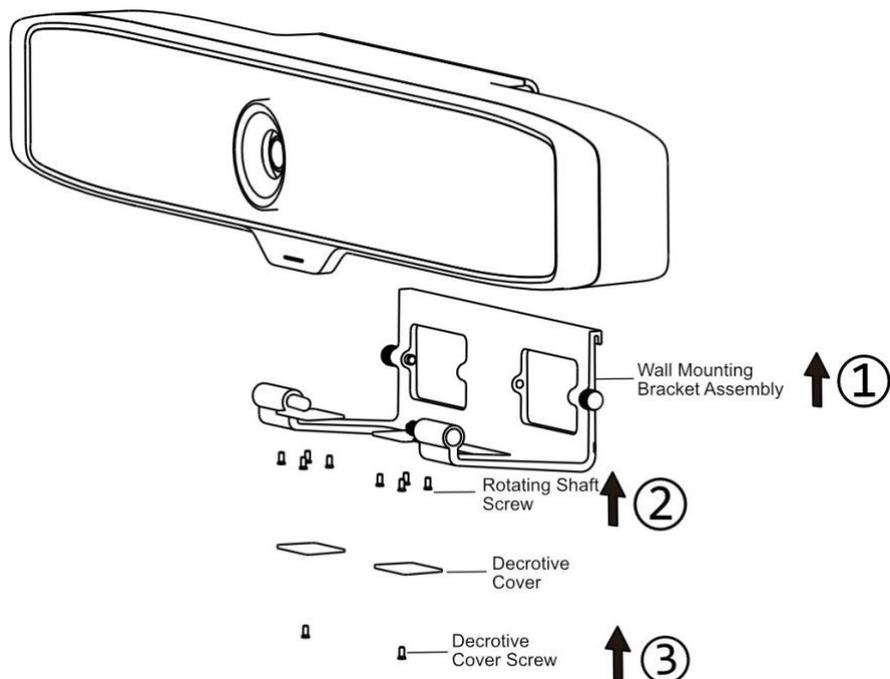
Instale el conjunto de soporte de montaje en pared
